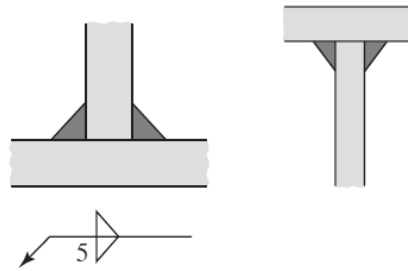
Soldaduras de filete; (Budynas & Nisbett, 2012)
